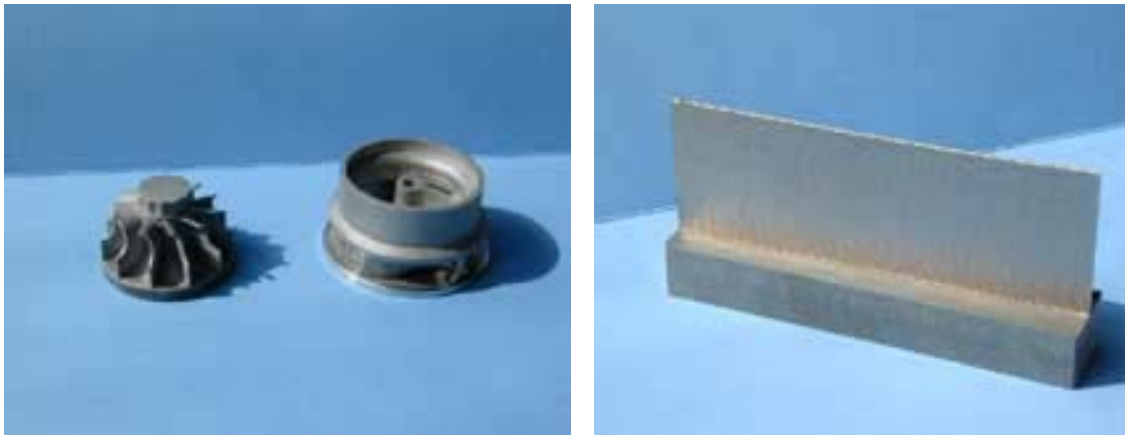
réparation de pièces et élaboration de parois par rechargement laser
